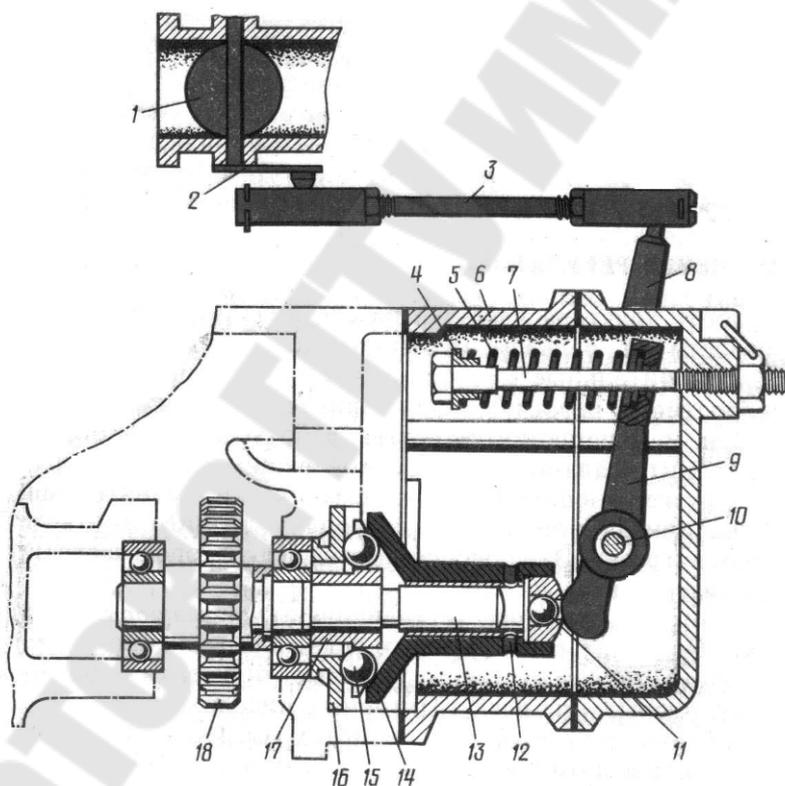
Однорежимный центробежный регулятор пускового двигателя П-10УД:
